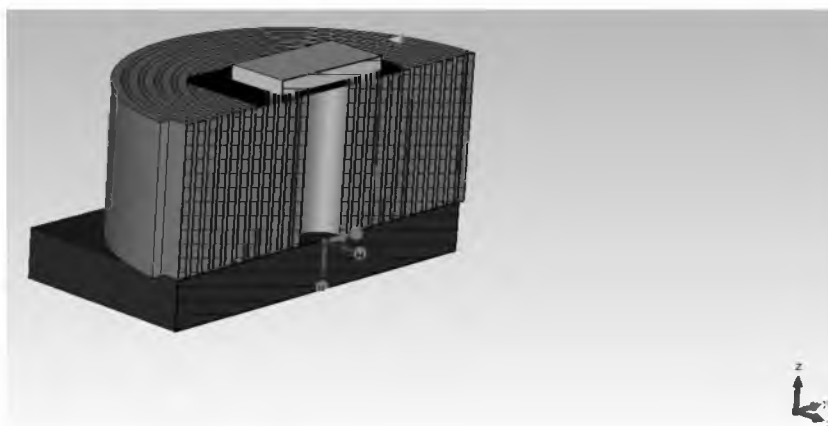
Разрез системы индуктор–заготовка. Параметры индуктора: толщина заготовки 15 мм, размеры 100 мм. Материал заготовки – алюминий
